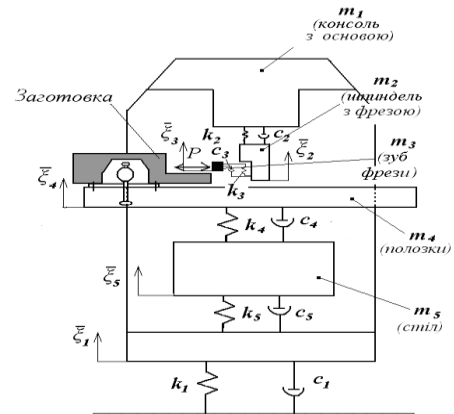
Динамічна модель обробної системи фрезерного верстата
